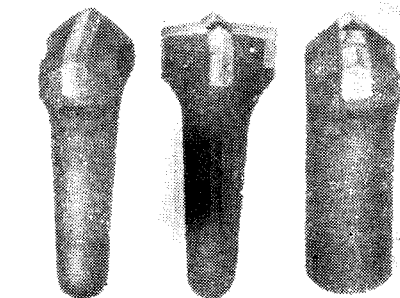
Коронки с твердосплавными вставками для бурового инструмента
